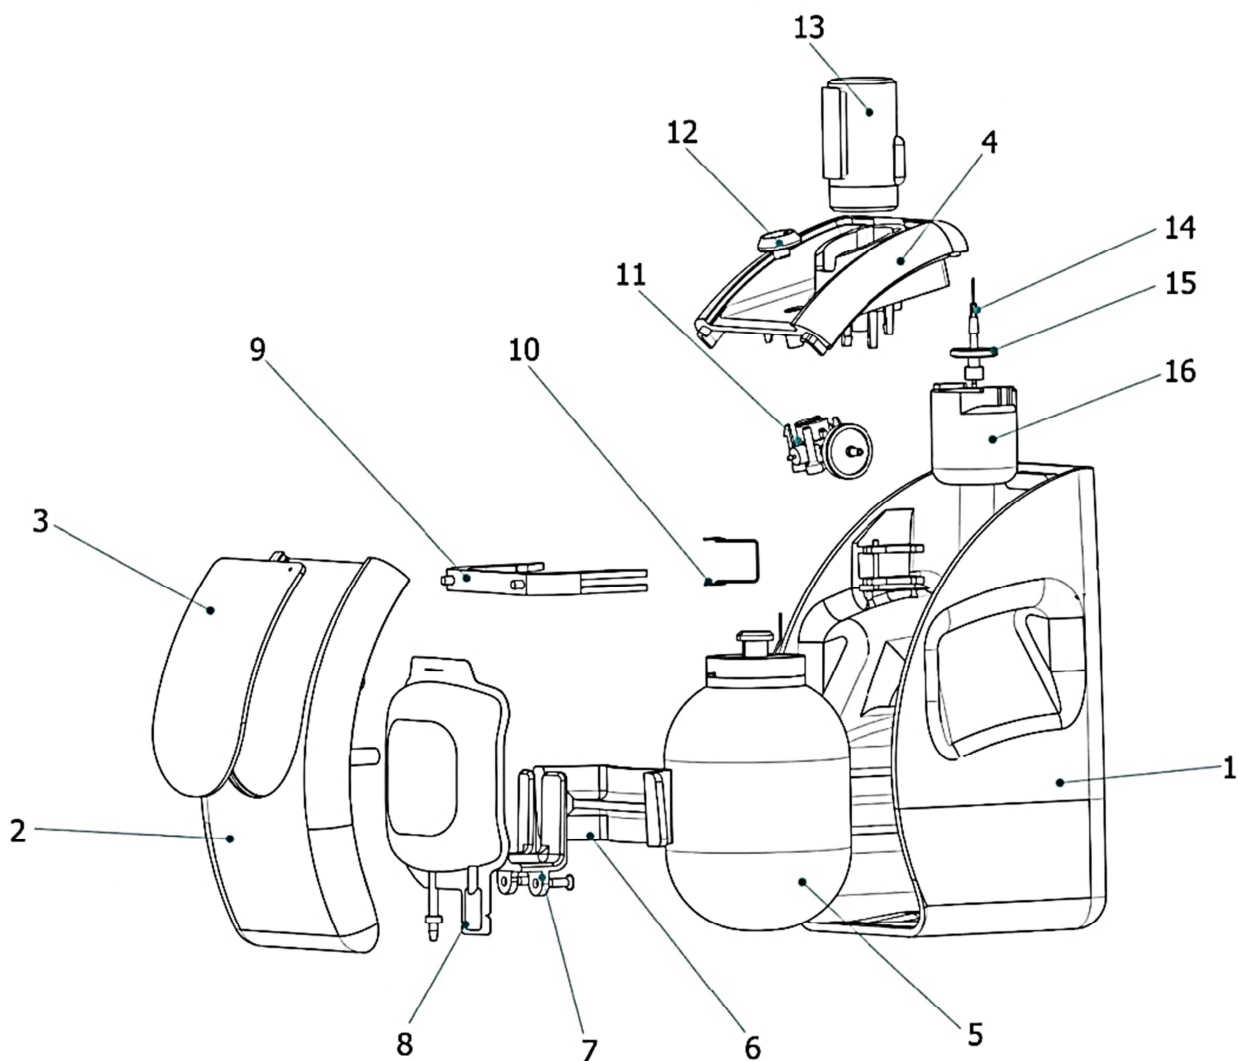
Схема корпуса и расположение в нем основных узлов генератора технеция: 1 – корпус; 2 – крышка 1; 3 – створка; 4 – крышка 2; 5 – биологическая защита колонки; 6 – фиксатор БЗ; 7 – держатель полимерного пакета; 8 – полимерный пакет с физиологическим раствором (0.9 % NaCl); 9 – защелка БЗ; 10 – пружина; 11 – система подачи раствор/воздух; 12 – регулятор подачи NaCl/Воздух; 13 – флакон в защитном контейнере; 14 – игла медицинская для элюации; 15 – фильтр жидкостный; 16 – защитный стакан
